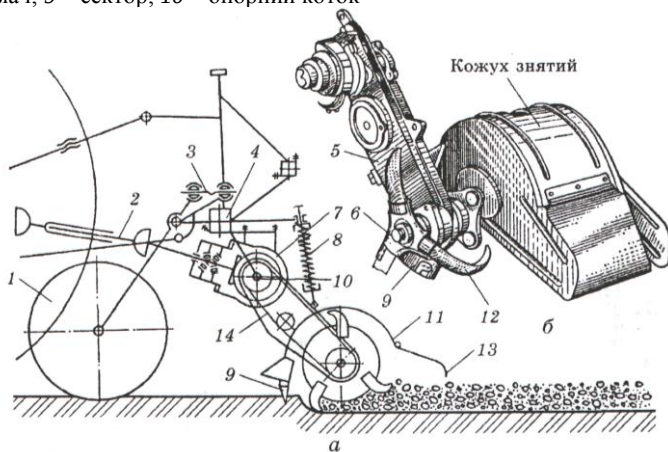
Культиватор фрезерний КФ-5.4:
